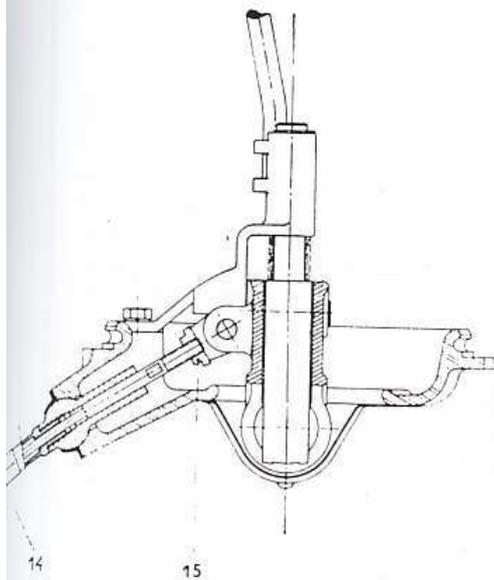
Vue en coupe du levier de vitesses et du câble de sélection
